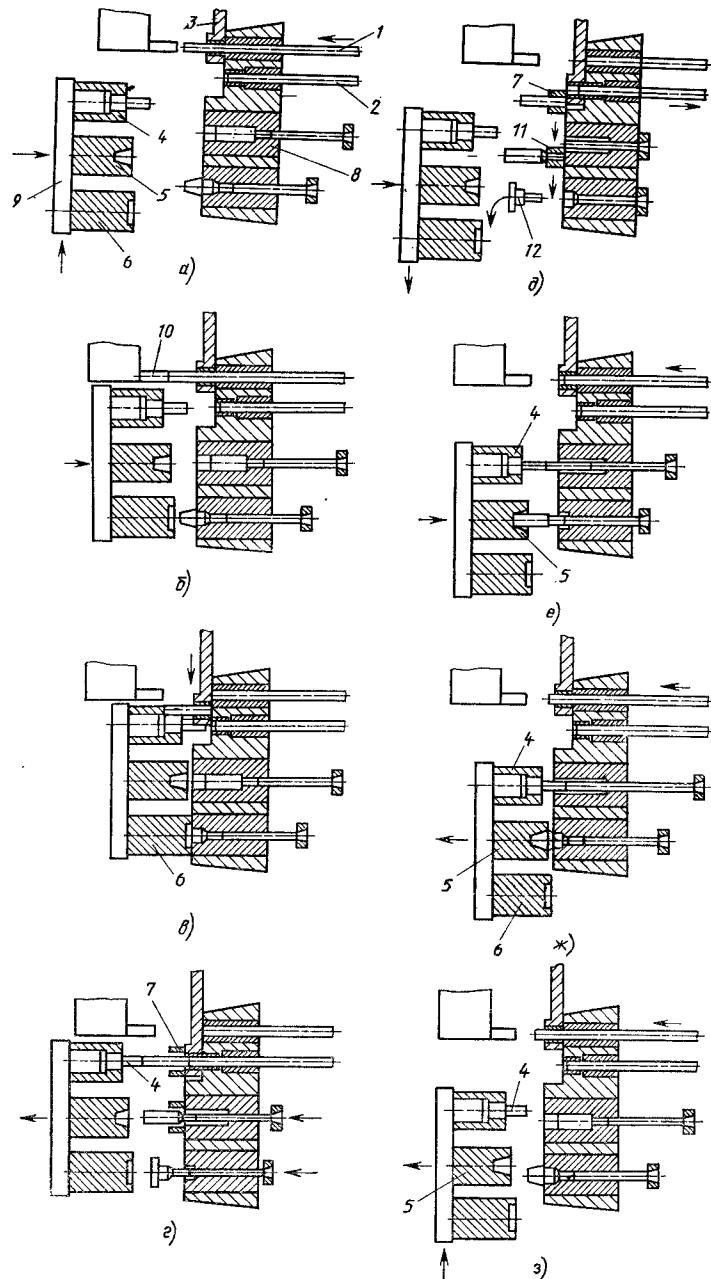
Схема штамповки детали на двухпозиционном трехударном автомате
